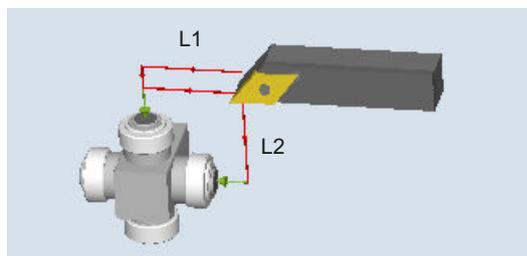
Messen: Drehwerkzeug (CYCLE982), Beispiel: komplett messen
